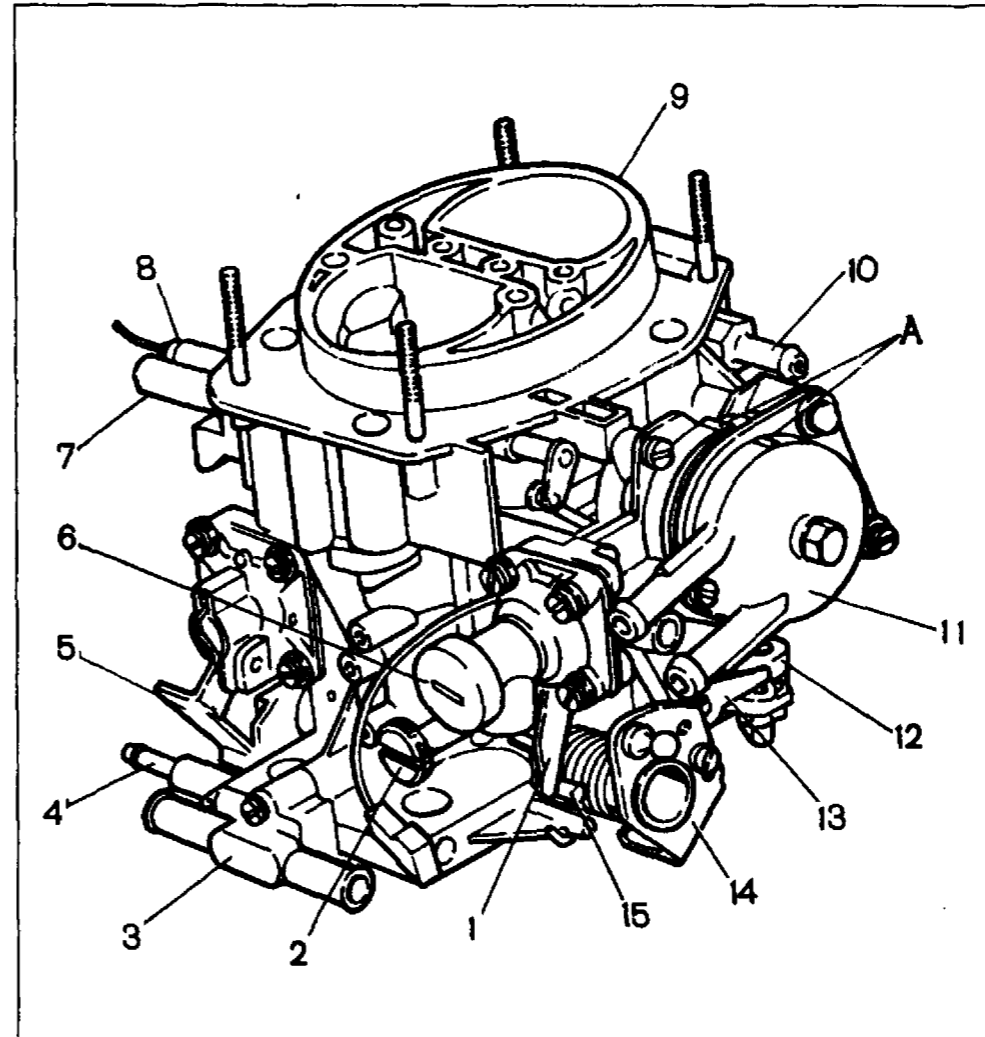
Внешний вид карбюратора 21083-1107010-62: 1 — рычаг привода блокировки второй камеры; 2 — регулировочный винт количества смеси холостого хода; 3 — блок подогрева карбюратора; 4 — патрубок вентиляции картера двигателя; 5 — рычаг привода ускорительного насоса; 6 — упор пускового устройства; 7 — патрубок отвода паров бензина из поплавковой камеры; 8 — актуатор системы холостого хода; 9 — крышка карбюратора; 10 — патрубок подвода топлива; 11 — полуавтоматическое пусковое устройство; 12 — корпус карбюратора; 13 — рычаг дроссельной заслонки второй камеры; 14 — рычаг управления дроссельными заслонками; 15 — штифт рычага блокировки второй камеры; А — метки для правильной установки биметаллической пружины пускового устройства
